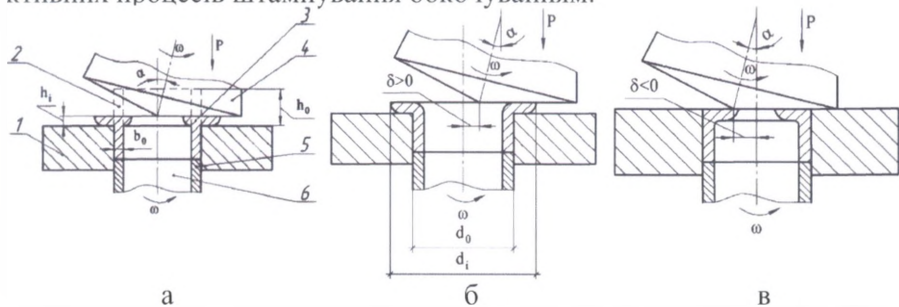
Положення валка і характерні геометричні параметри заготовки при висаджуванні розкочуванням буртів: а – зовнішніх і внутрішніх; б – зовнішніх; в – внутрішніх; 1 – матриця; 2 – заготовка; 3 – виріб; 4 – валок; 5 – штовхач; 6 – оправка
